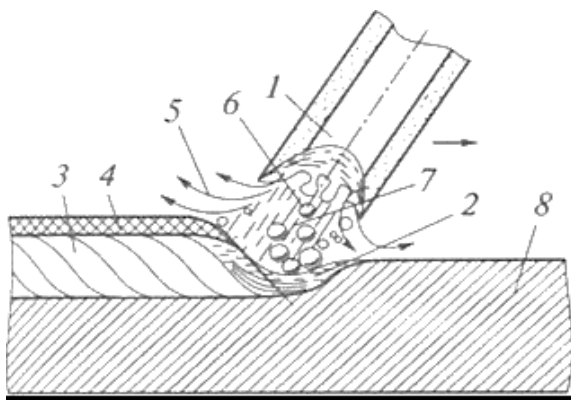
Схема газослаковой защиты металла при сварке электродами с покрытием:
